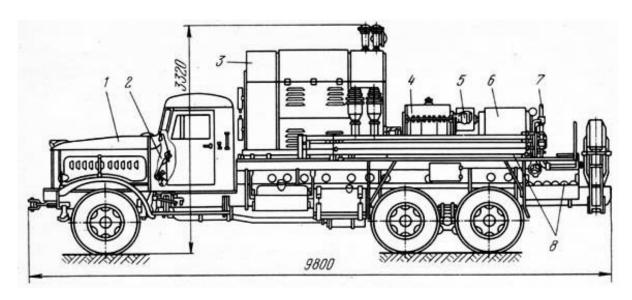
Насосный агрегат для ГРП 4АН-700: 1 - автомобиль КрАЗ-257; 2 - кабина управления; 3 - силовой агрегат; 4 - коробка скоростей; 5 - муфта сцепления; 6 - насосный агрегат; 7 - выкидной маинфольд; 8 - соединительные трубы высокого давления
